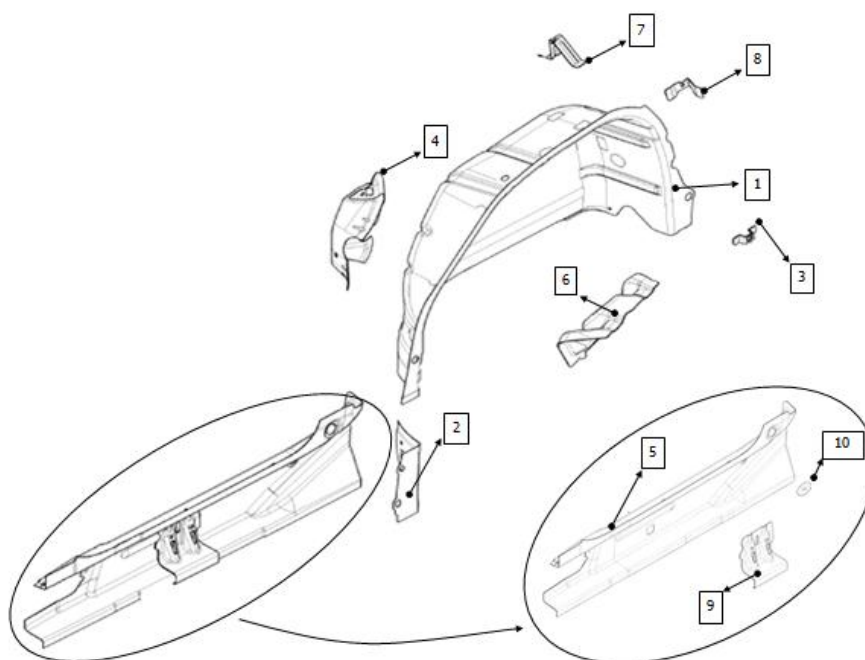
Componentes que constituem o produto acabado Cava da roda esquerda
